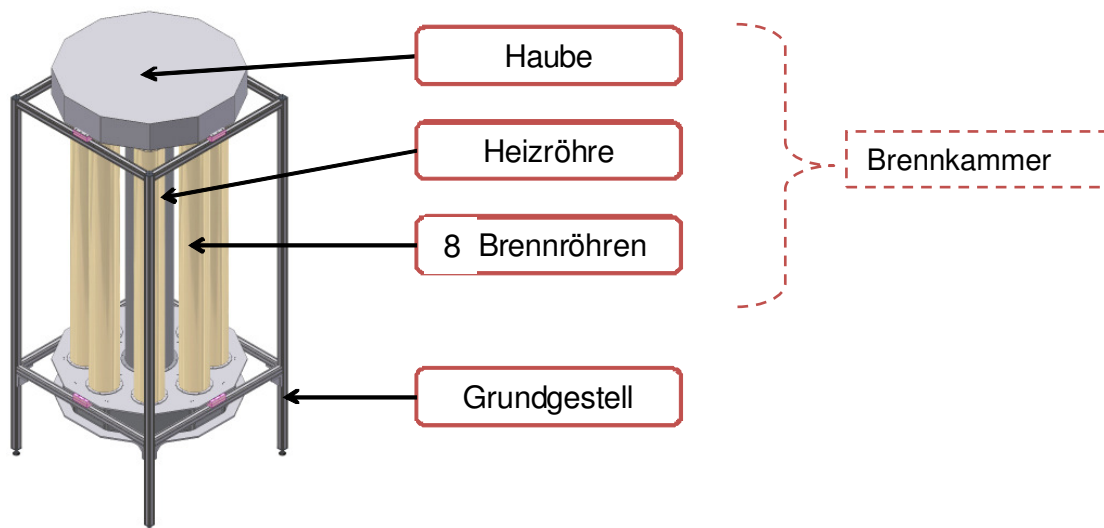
Bauweise des Orgelpfeifenofens mit Brennkammer und Grundgestell
